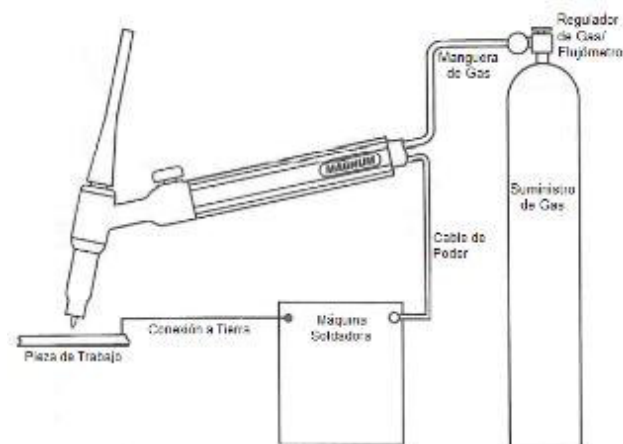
Configuración completa de la soldadura GTAW. [5]
